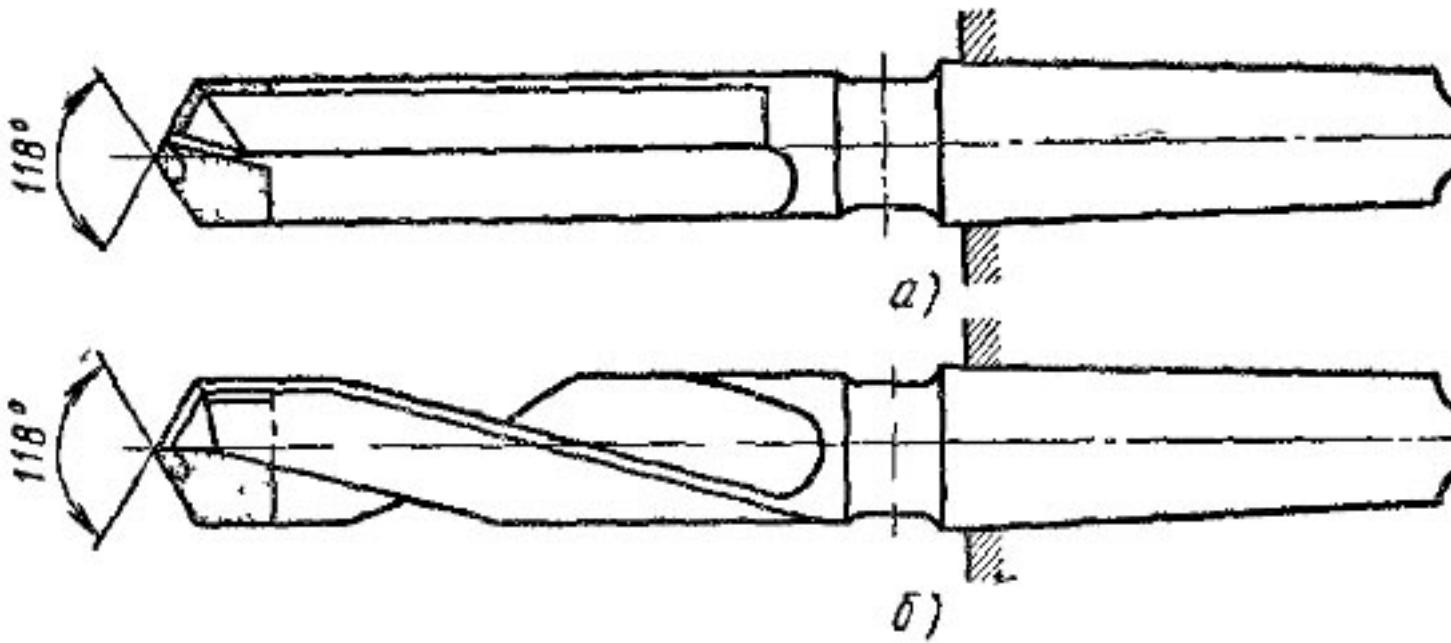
Сверла, оснащенные пластинками из твердого сплава
